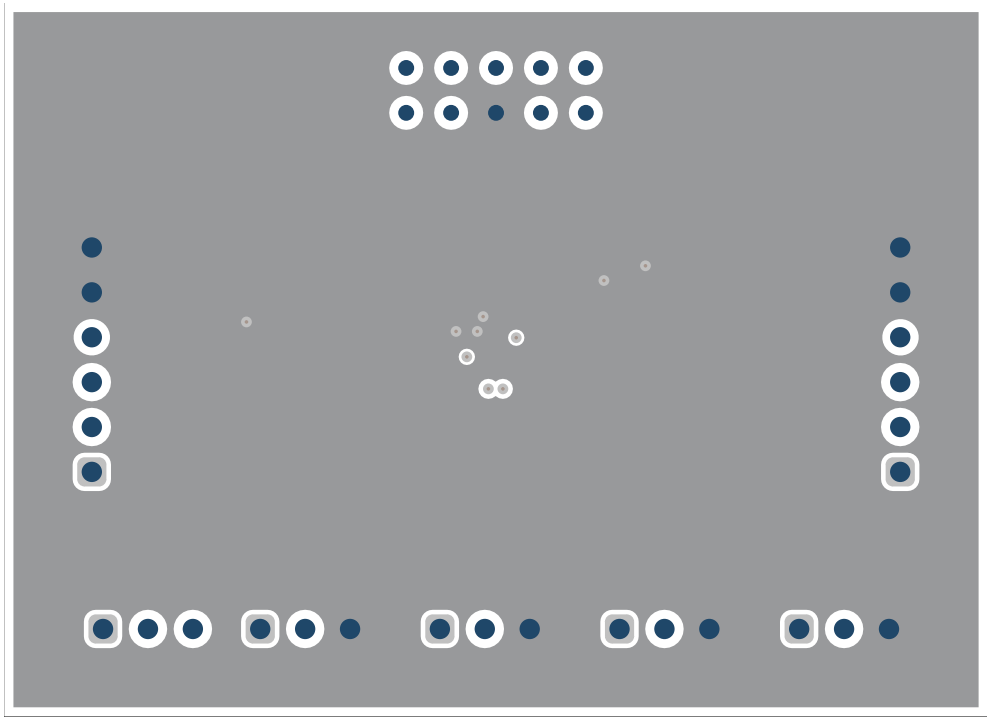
TPS6286x1EVM PCB - 信号层 1 (顶视图)
